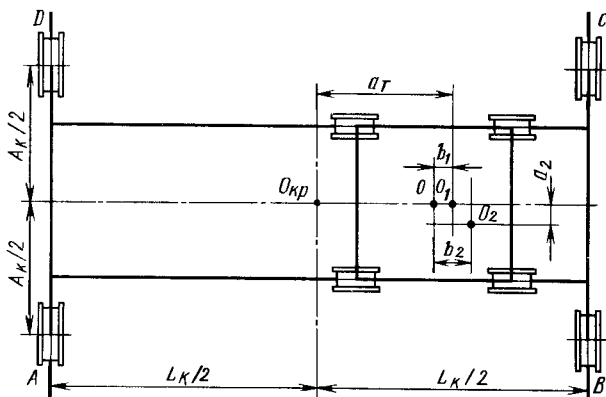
Расчетная схема определения вертикальных нагрузок на ходовые колеса моста крана
